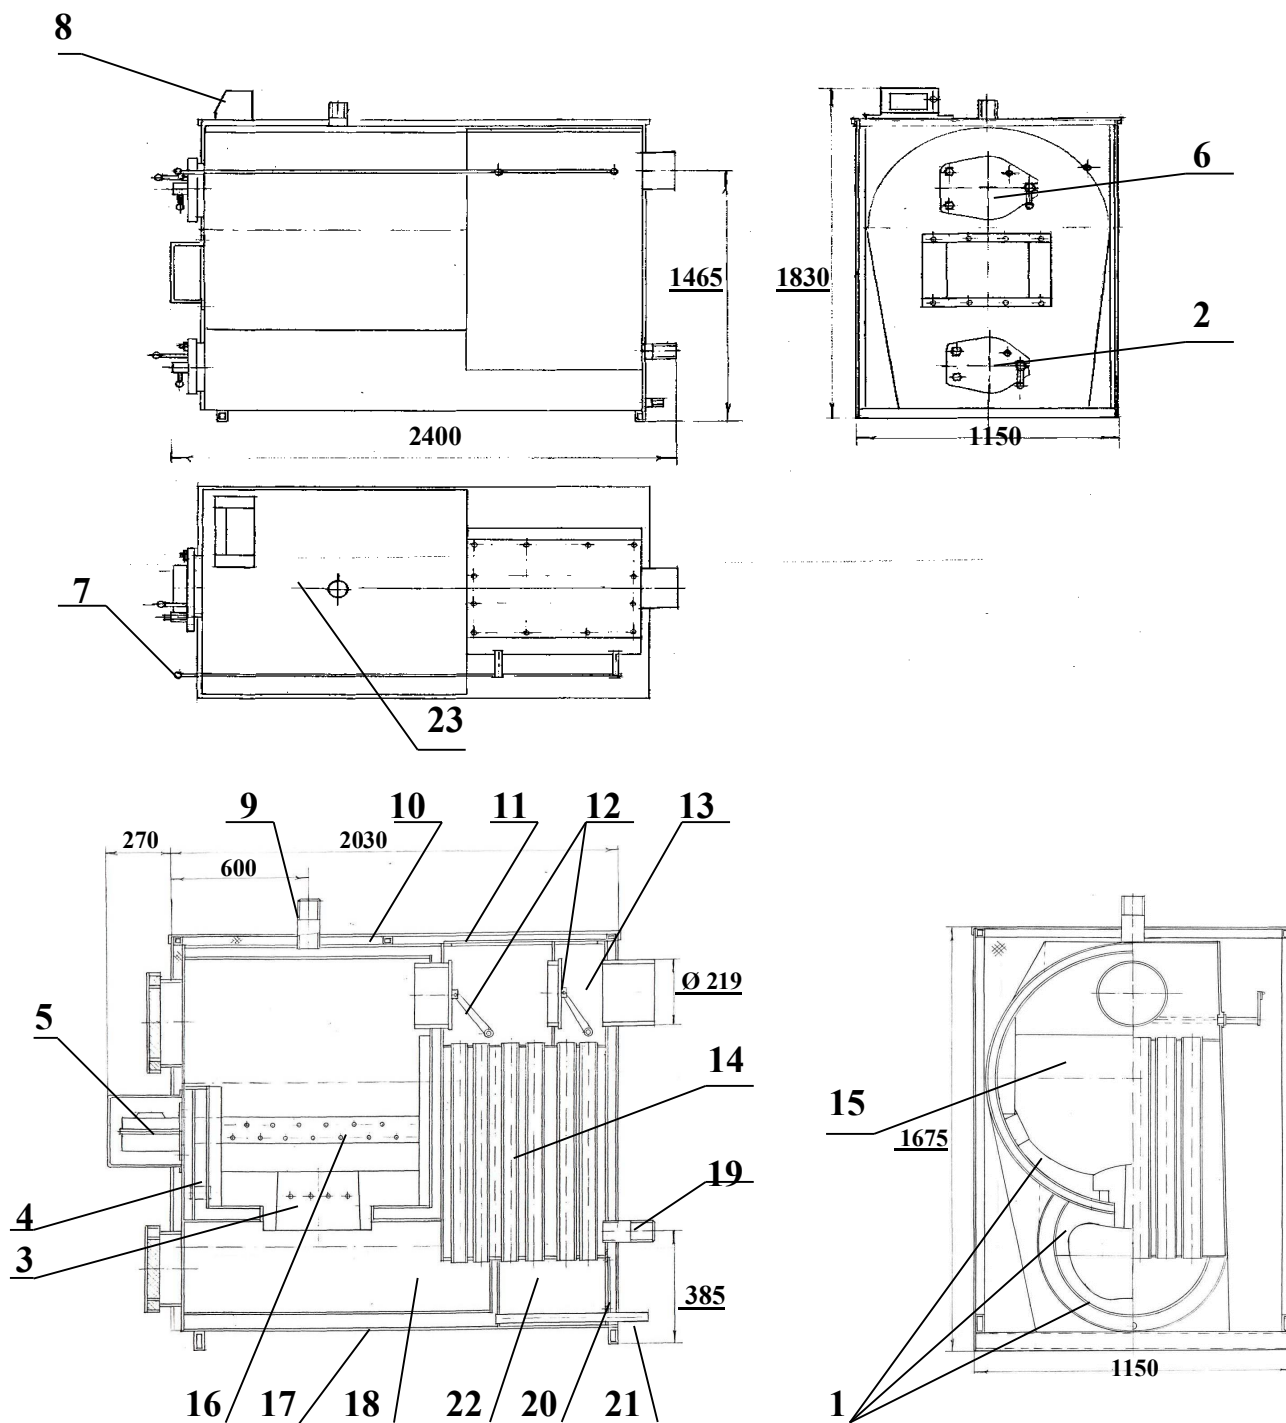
Устройство котла. Общий вид, продольный и поперечный разрез.
